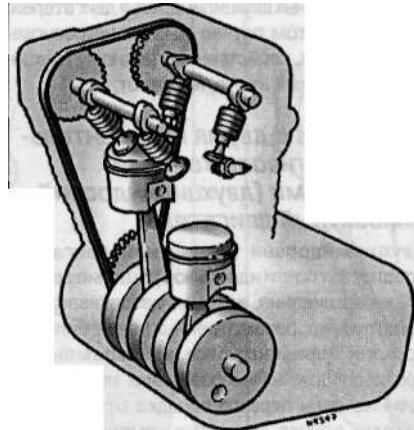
б Четырехтактный рядный двухцилиндровый двигатель с чередованием вспышек через 180 градусов
